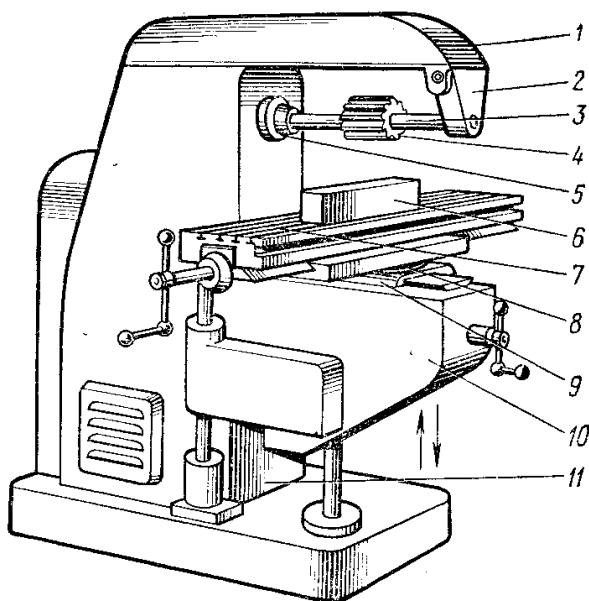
Зовнішній вигляд горизонтально-фрезерного верстату
